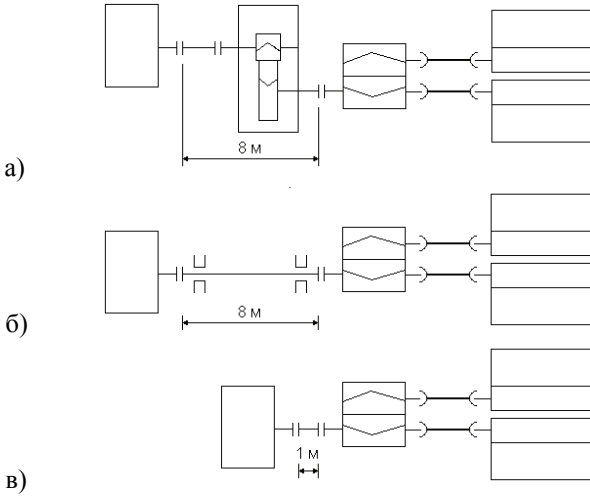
Схема линий привода прокатных клетей чистой группы: а) существующая схема с редуктором, б) замена редуктора длинным промежуточным валом, длиной 8 м, в) установка электродвигателя непосредственно на место редуктора, промежуточный вал длиной 1 м.
